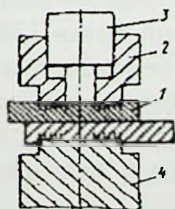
Схема точечной сварки с односторонним деформированием свариваемых деталей.
